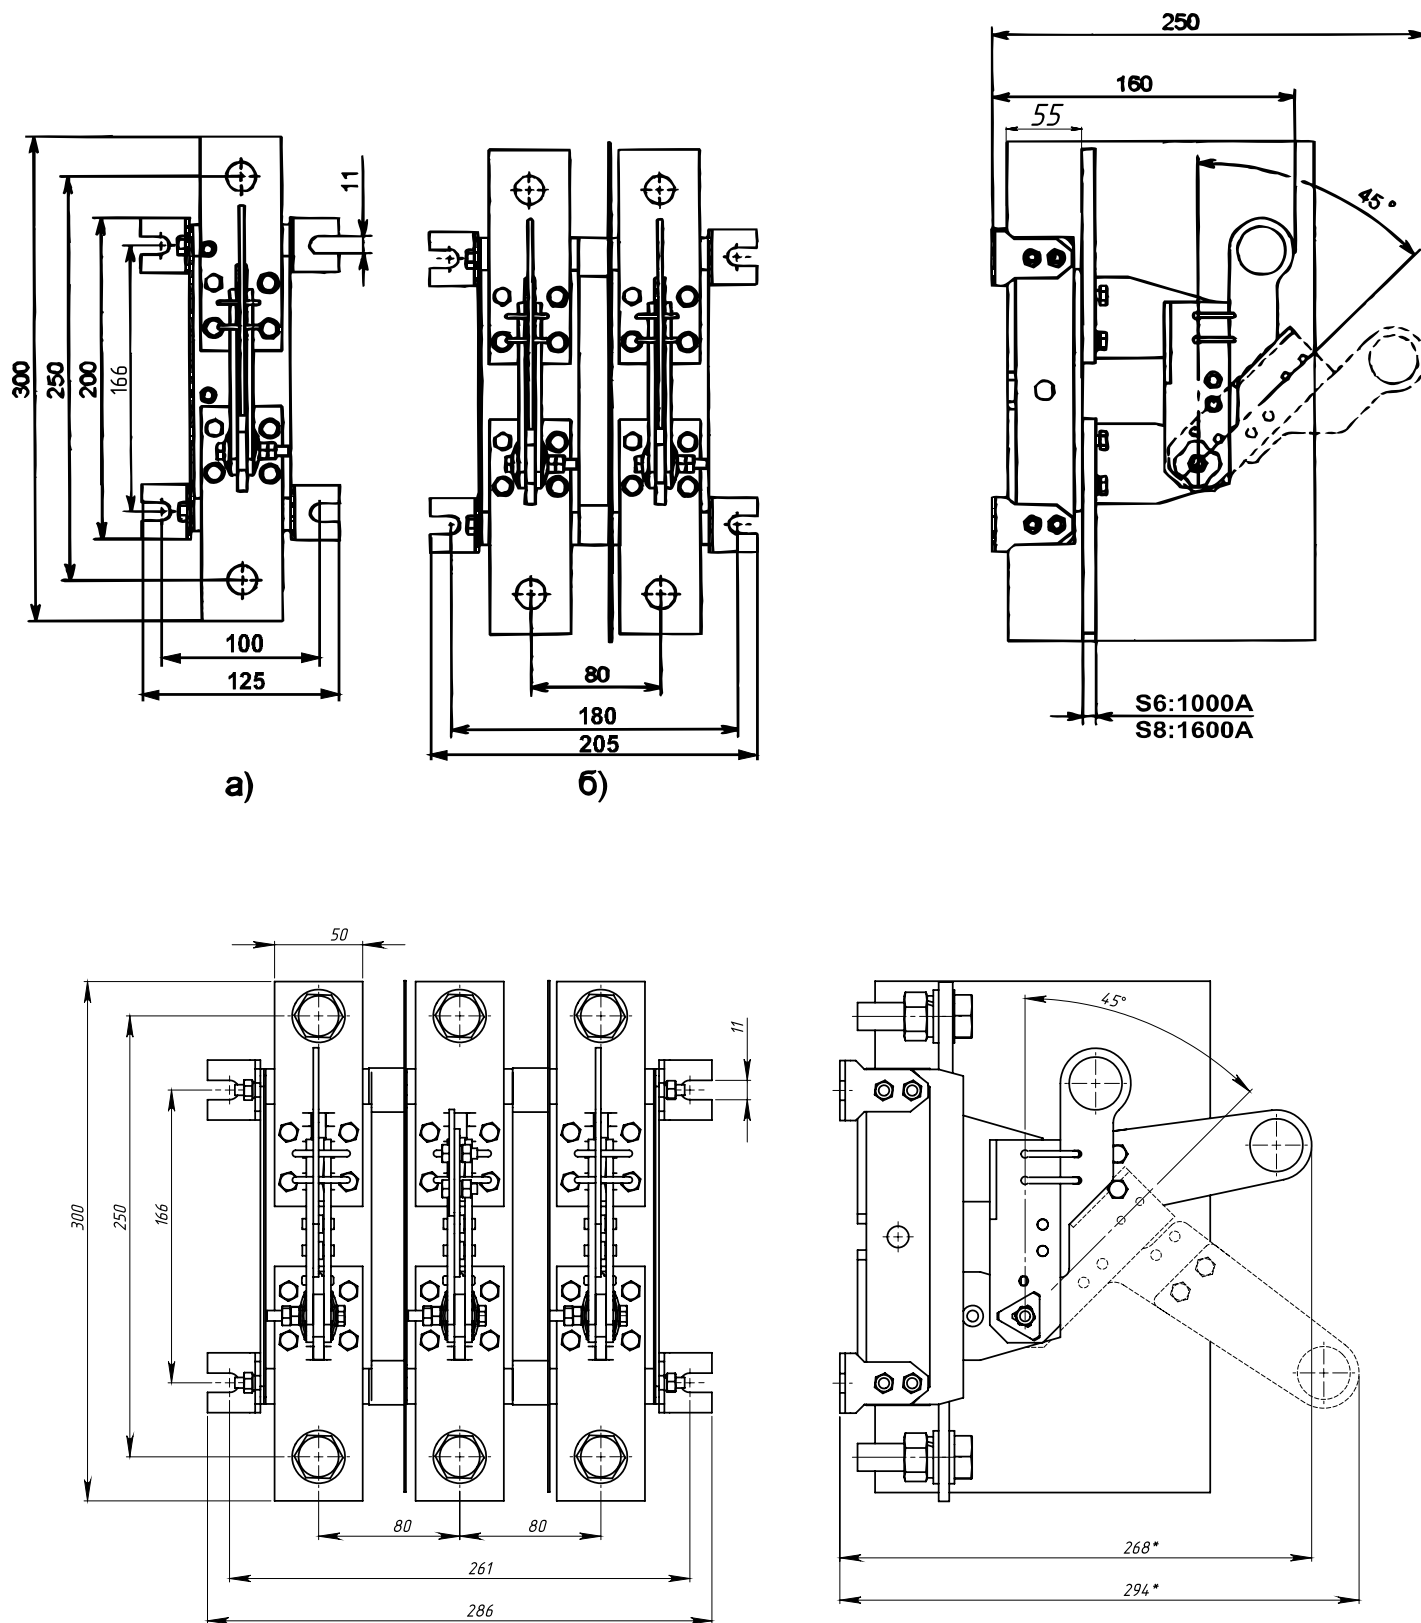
Разъединитель PE19 с рычагом для полюсного оперирования штангой
